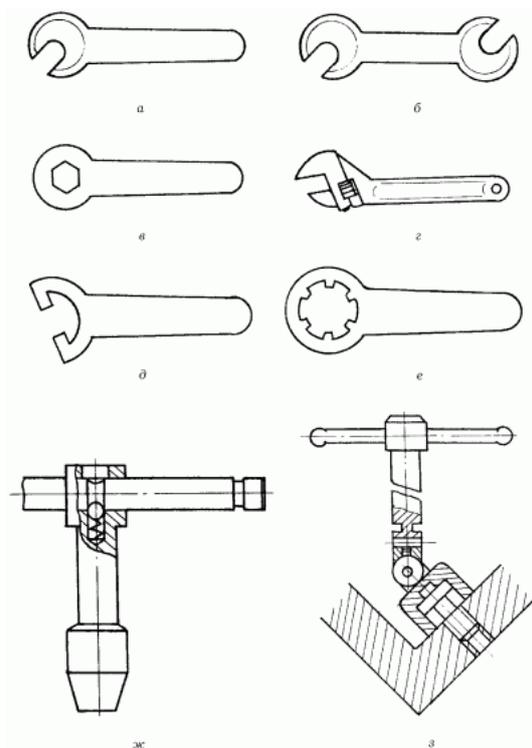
Ручной инструмент для сборки резьбовых соединений.
